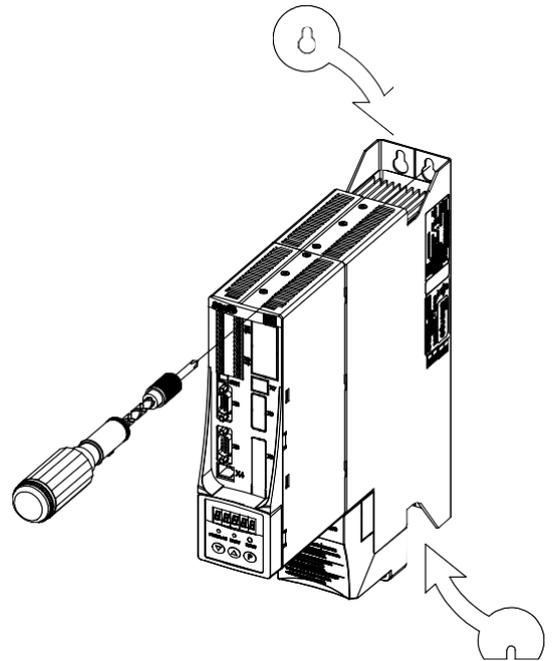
Instalação do SCA-05 em placa de montagem
